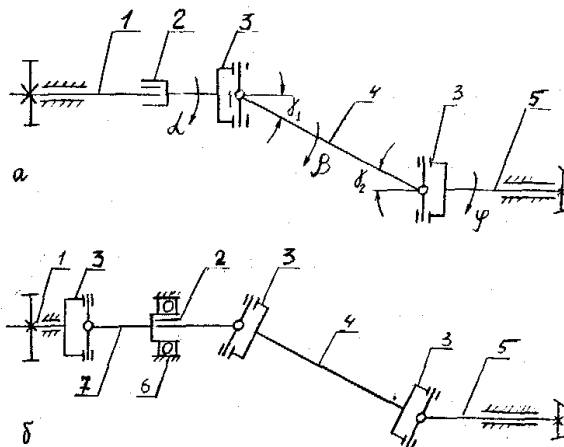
Кінематичні схеми карданних передач: а – з двома карданними шарнірами; б – трьома карданними шарнірами; 1 – вторинний вал коробки передач; 2 – компенсуючий пристрій; 3 – карданний шарнір; 4 – основний карданний вал; 5 – вал ведучої шестерні головної передачі; 6 – проміжна опора; 7 – проміжний вал
